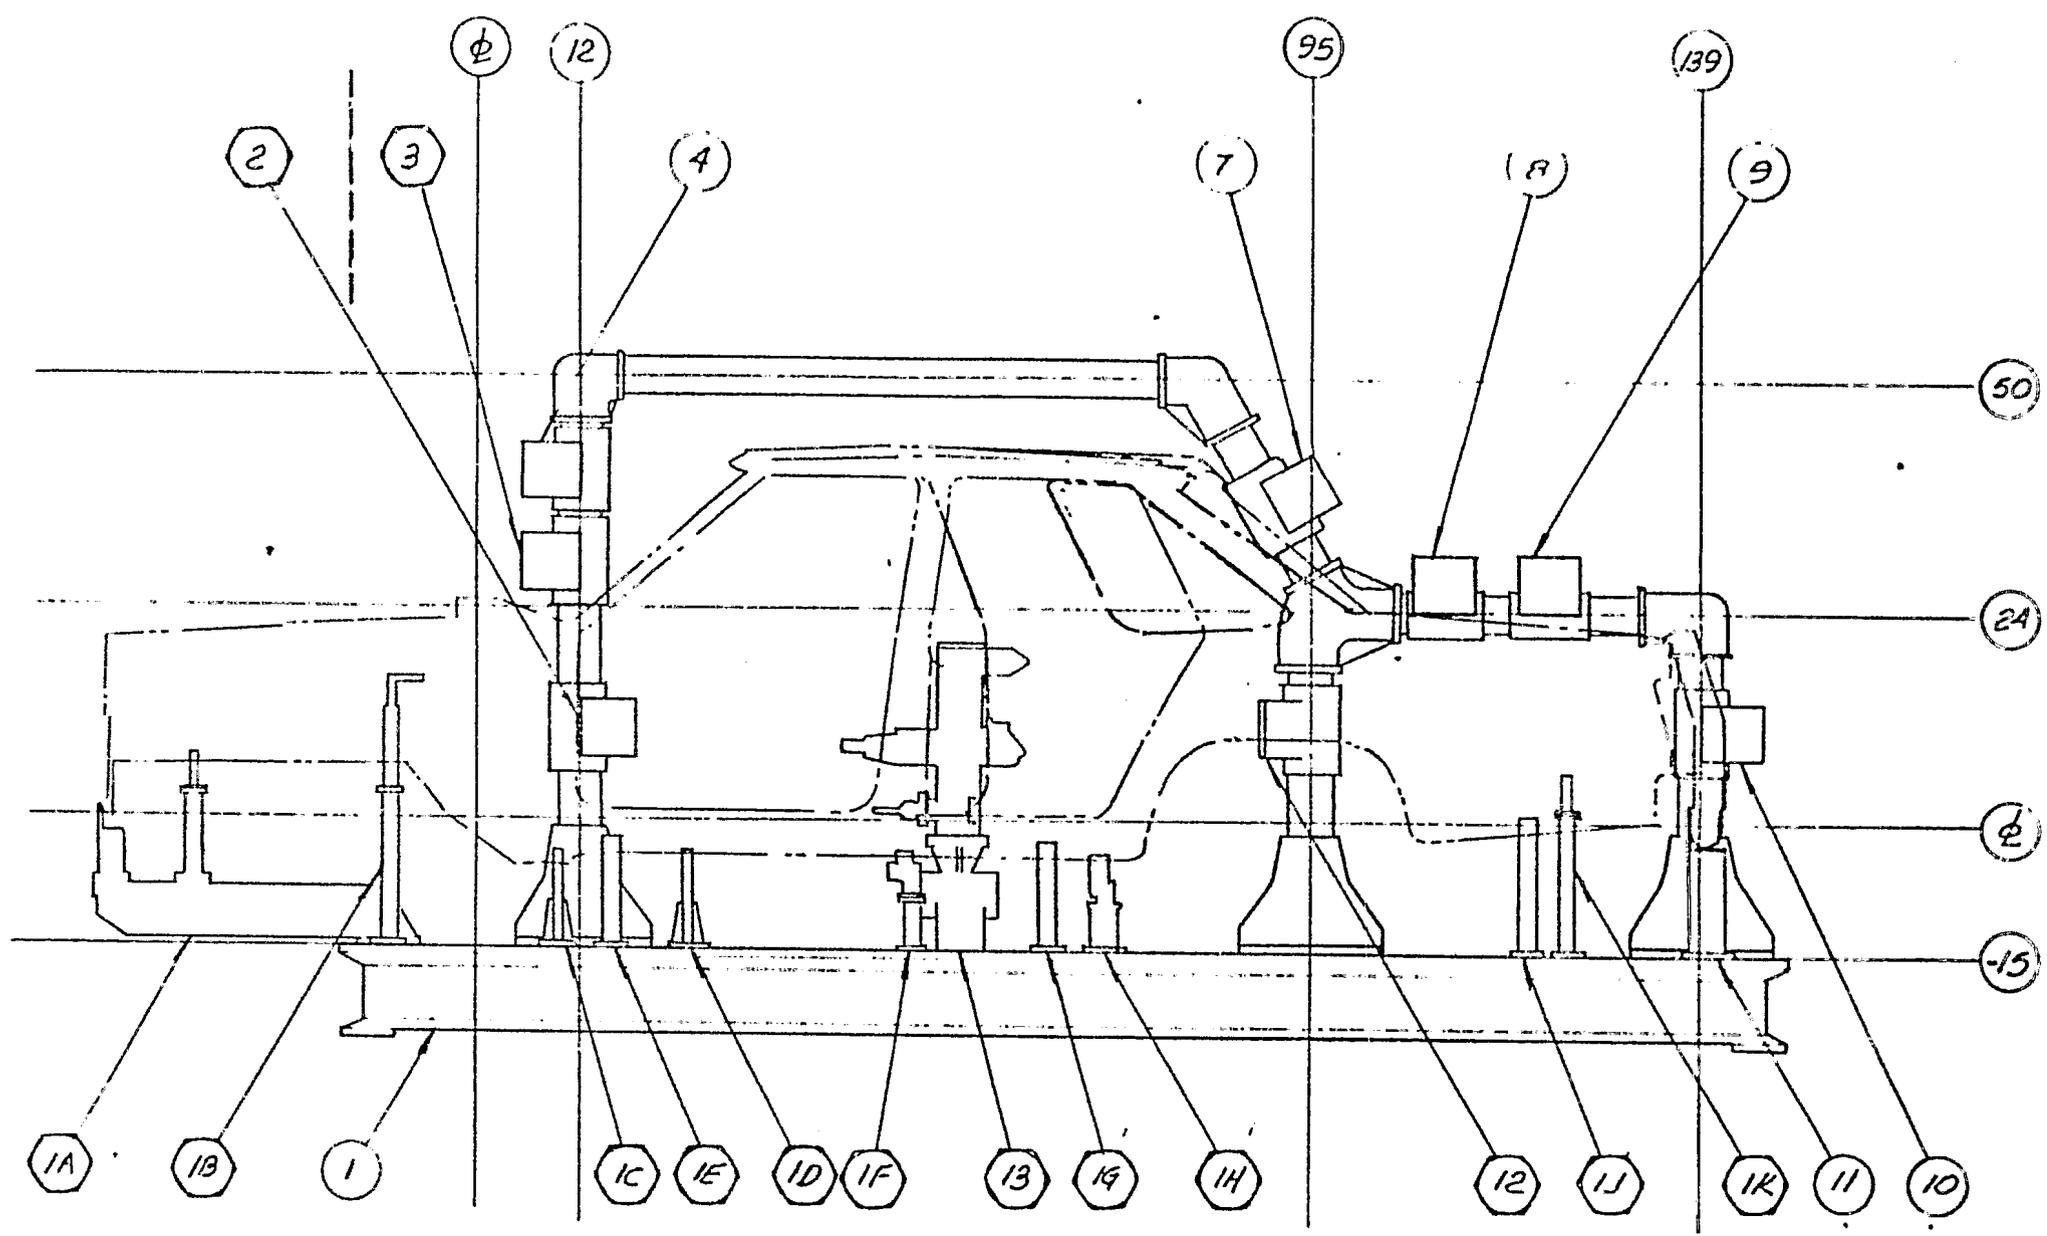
PARTES COMPONENTES DEL ENSAMBLE DE UNA CARROCERIA
